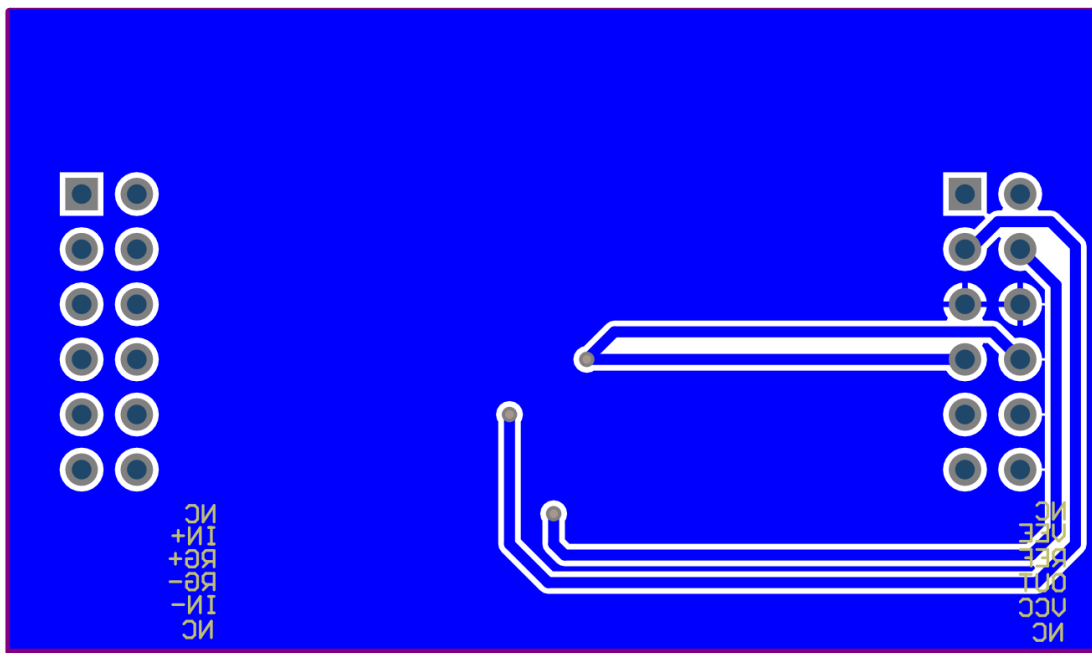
ZJA3620/22/3628 评估板 PCB 底层设计
